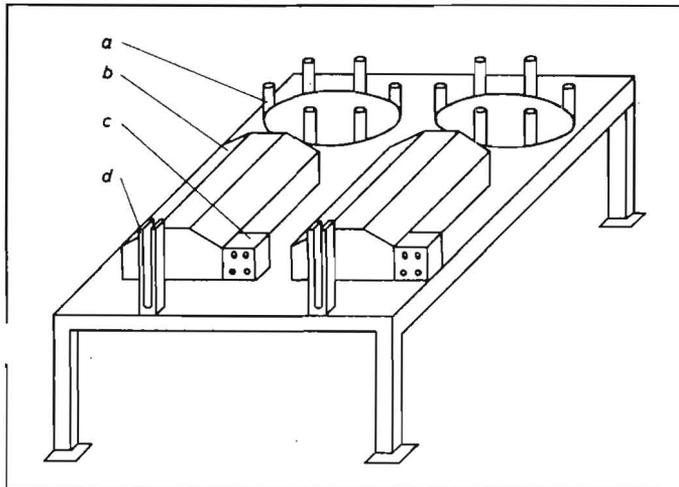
Montagearbeitsplatz für Kolben und Pleuel;
